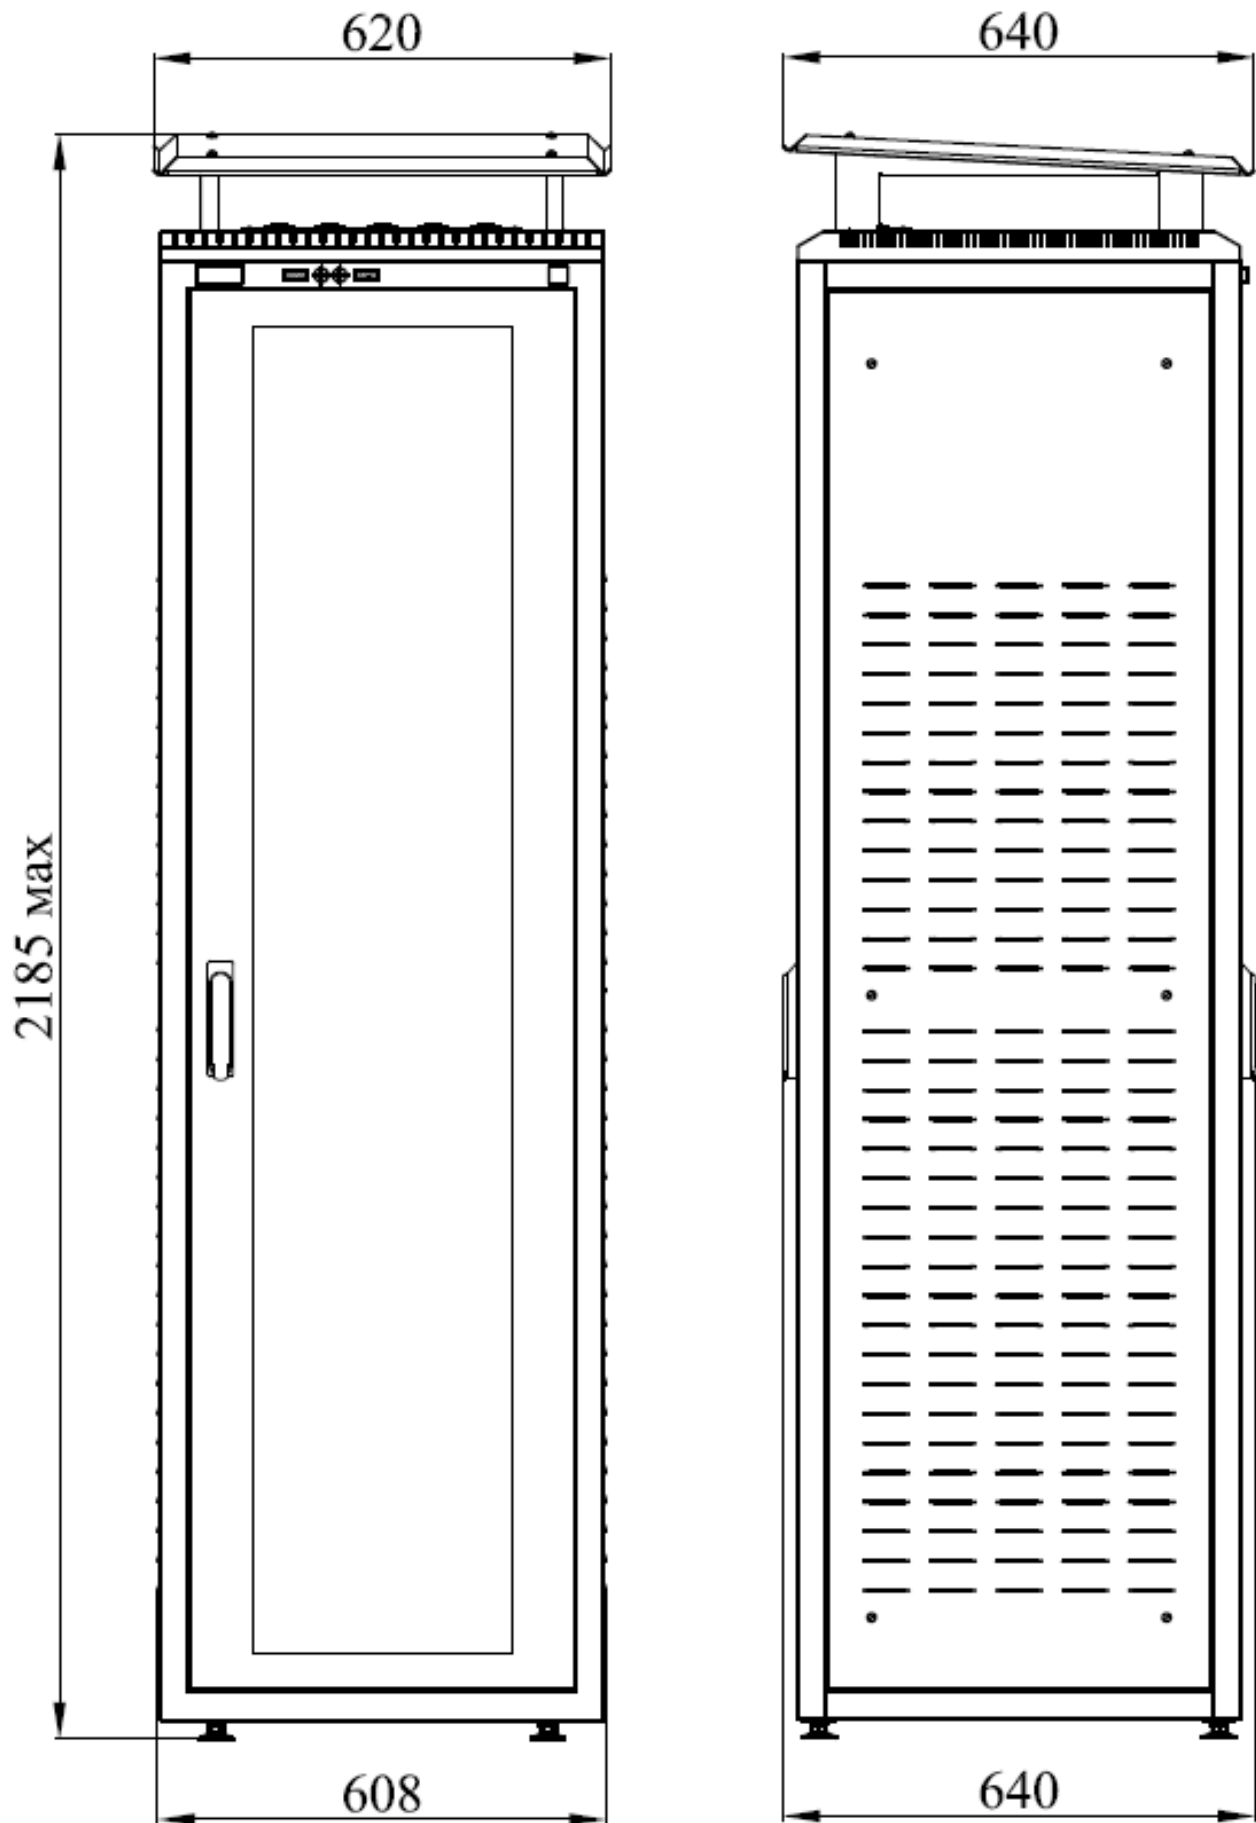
Габаритные размеры стойки ЦМ КРЦ-М с навесом и без цоколя
